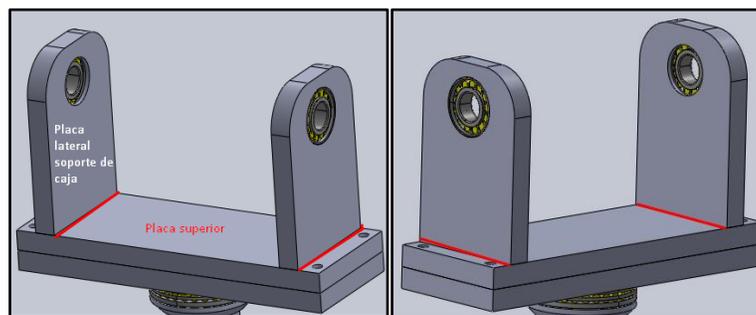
Ubicación del cordón de soldadura entre la placa superior y la placa lateral.
